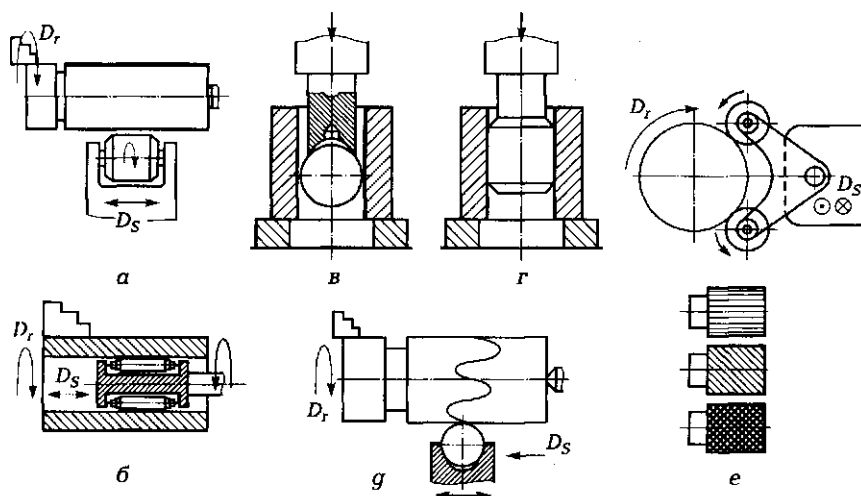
Схемы обработки заготовок без снятия стружки:
